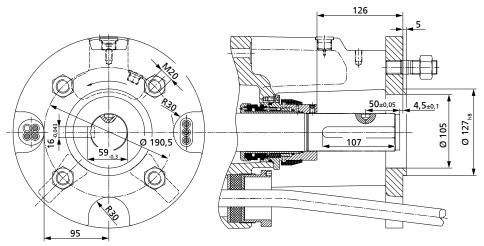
Dimensiones de conexión de UMA 300, 2 polos, dimensiones indicadas en [mm]
